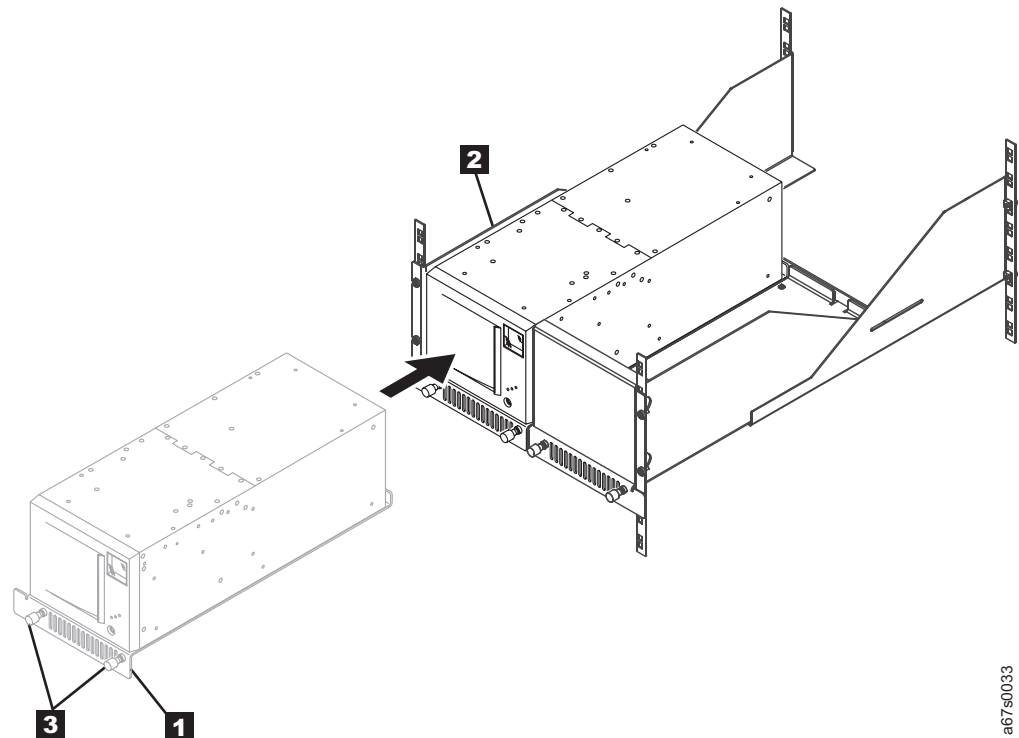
Schlitten in Gehäuseeinbaufach installieren
